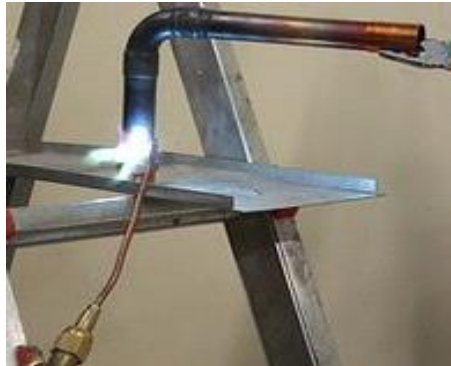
[Soldadura Oxiacetilénica](#)
